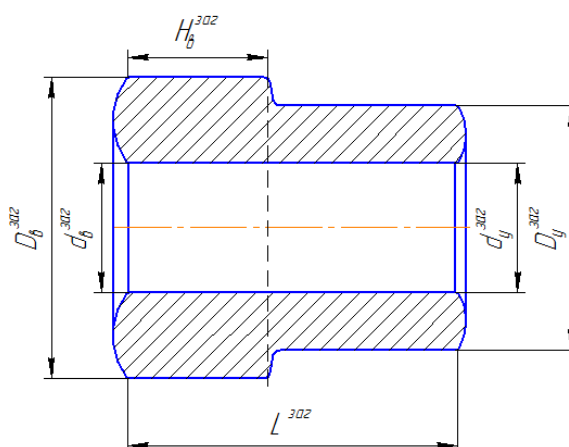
Ескіз заготовки для кування конусних втулок з умовними позначеннями
